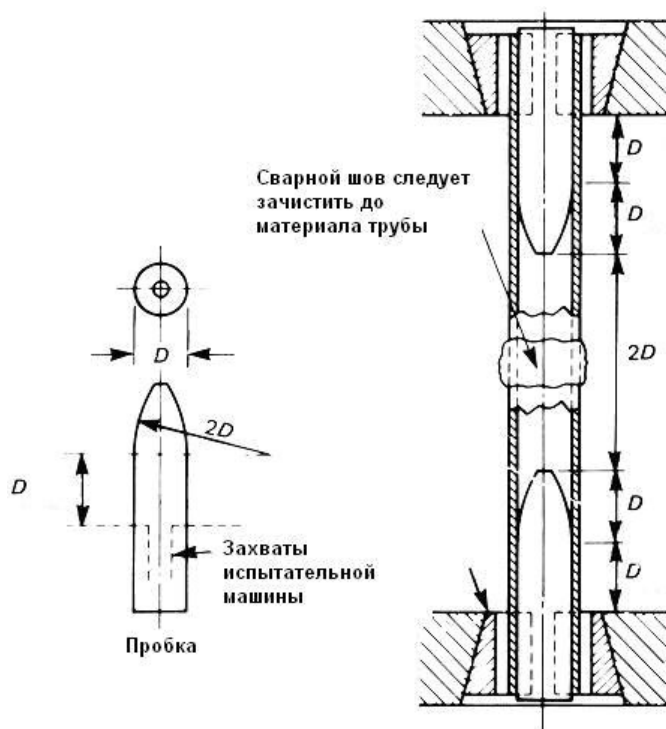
Стандартная схема подготовки образца к испытаниям.
